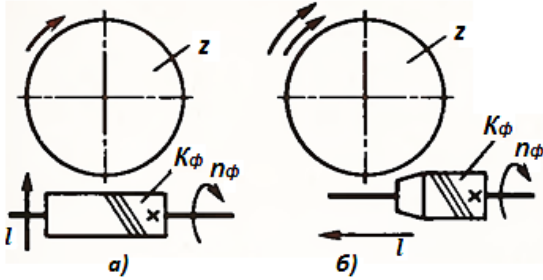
Схеми встановлення черв'ячної фрези для фрезерування черв'ячних коліс
